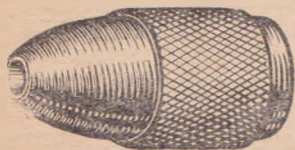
Калибромер для калибровки пуль 5,6-мм патронов
